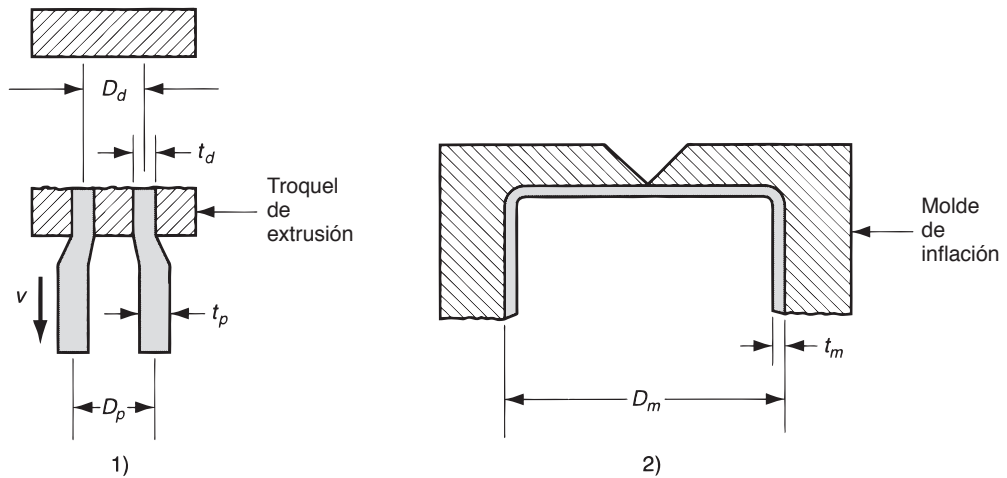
1) Dimensiones del troquel de extrusión, mostrando el parison después de la expansión del troquel, y 2) contenedor moldeado por soplado, en el moldeo soplado por extrusión.
